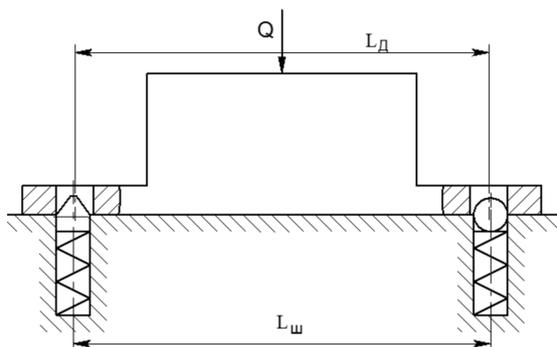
Установка заготовки на один конусный палец и сферическую поверхность
